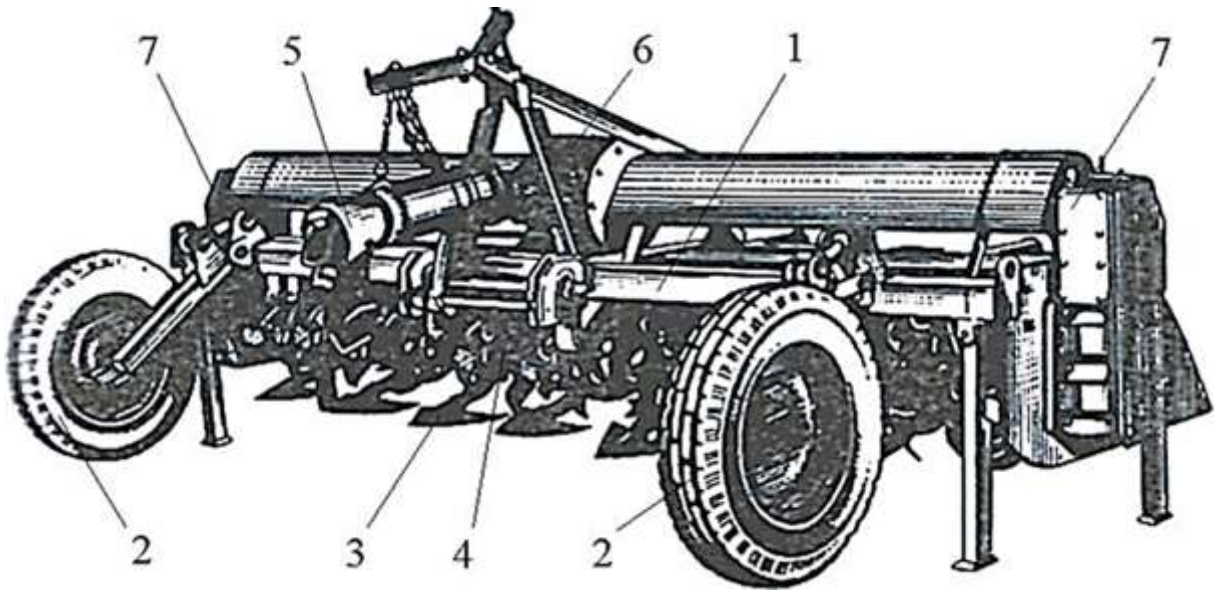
Загальний вигляд комбінованого агрегата з активними робочими органами АКР-3,6
